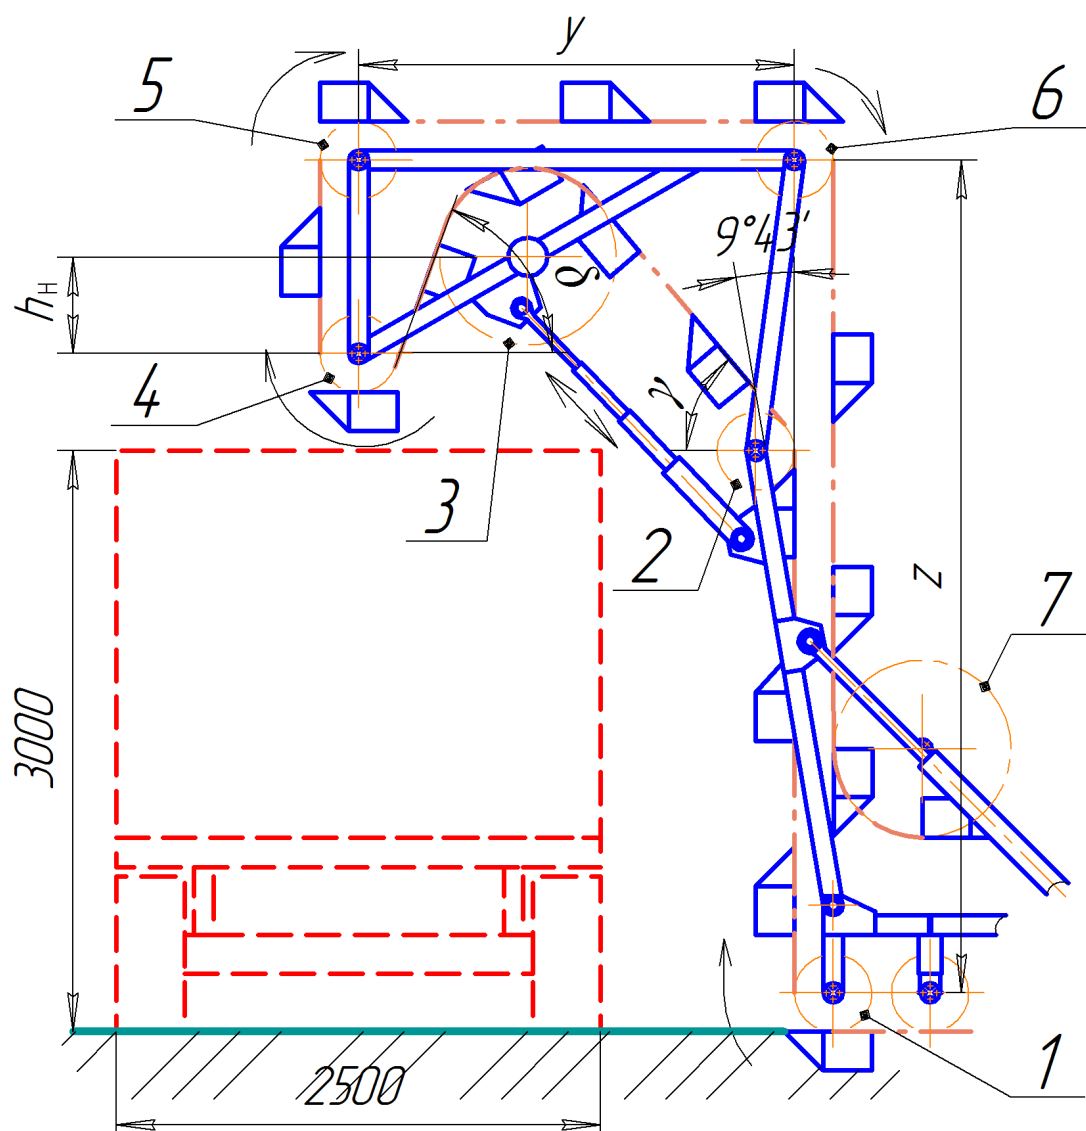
Конструктивная компоновка загрузочной части агрегата:
